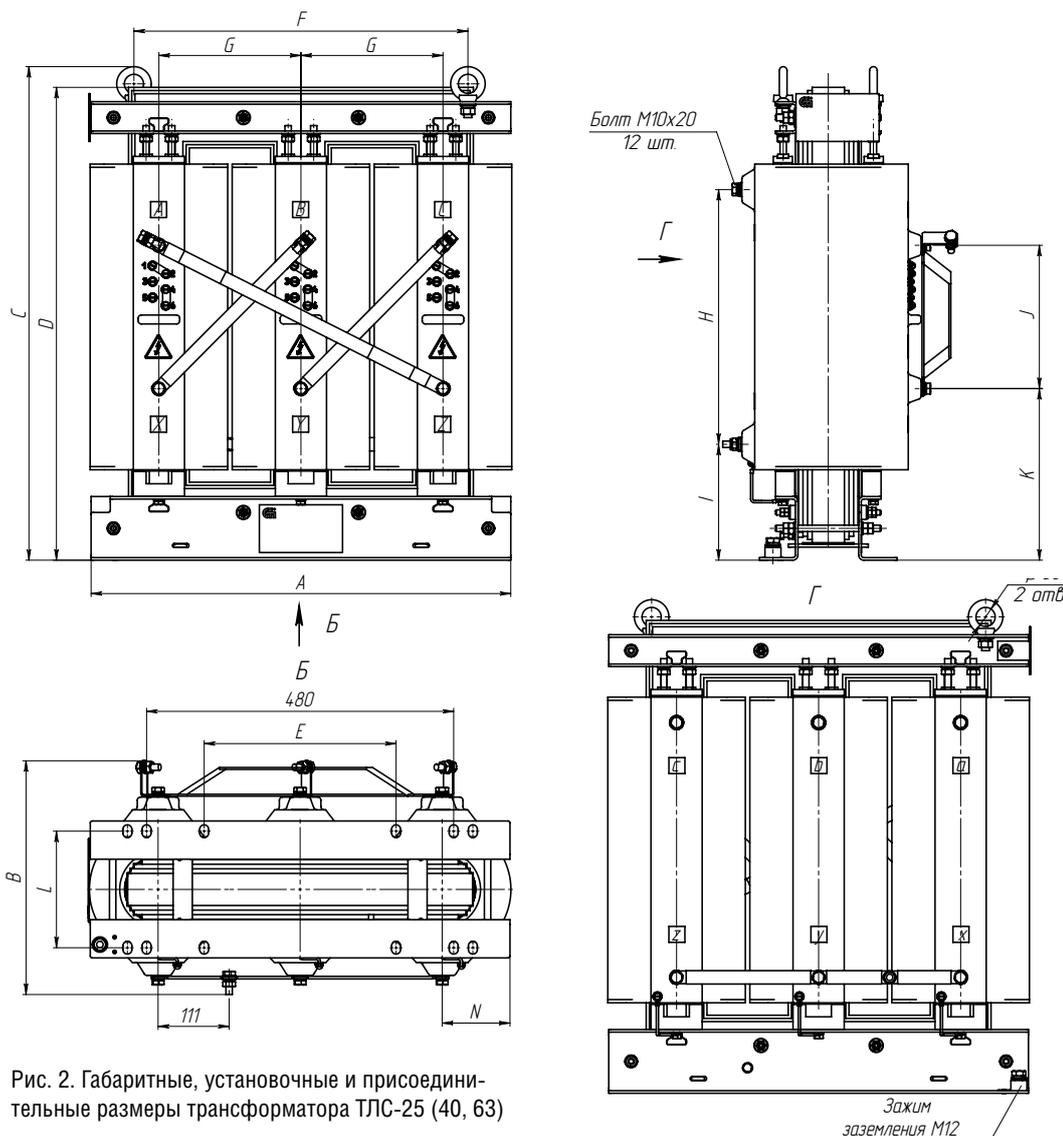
Габаритные, установочные и присоединительные размеры трансформатора ТЛС-25 (40, 63)
